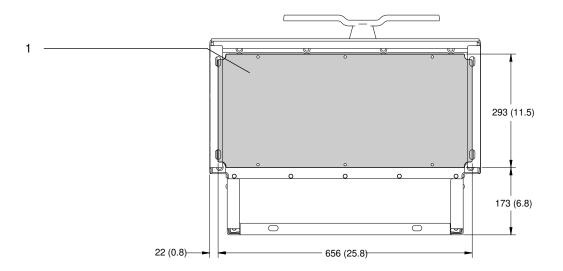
Espace pour la porte et dimensions de la plaque d'entrée des câbles pour E2h
